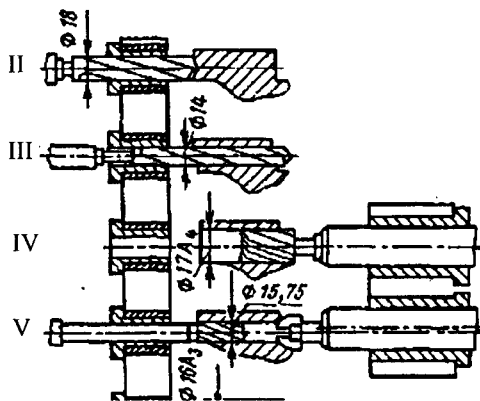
Схема обробки отворів під шатунні болти на агрегатно-свердлильному автоматі.
